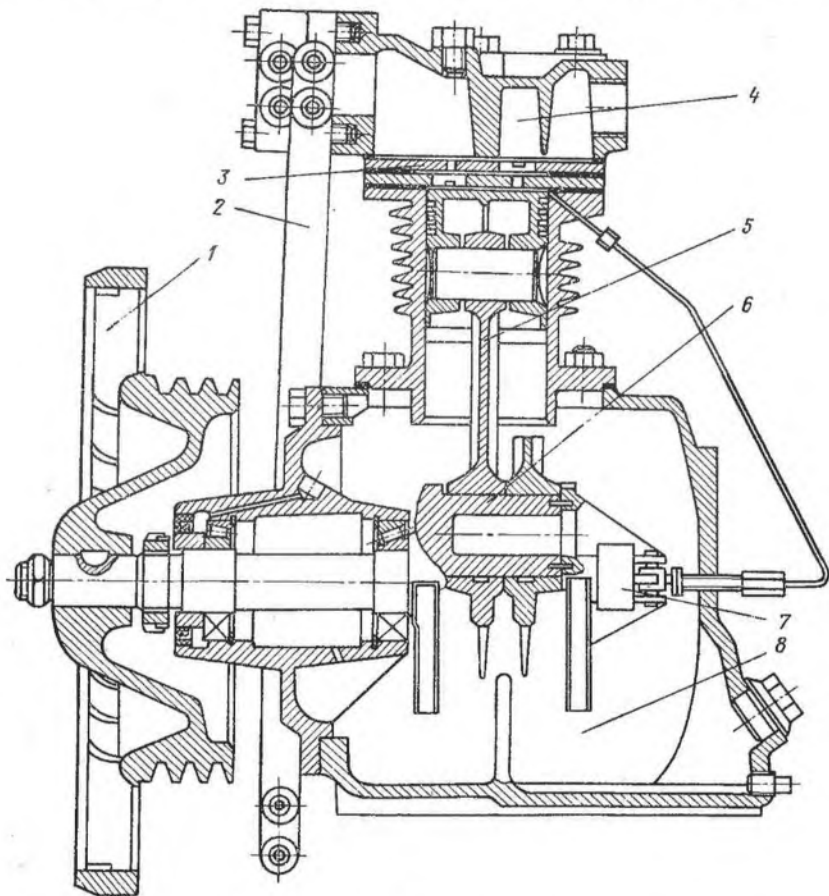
Продольный разрез У-образного компрессора с консольным коленчатым валом:
